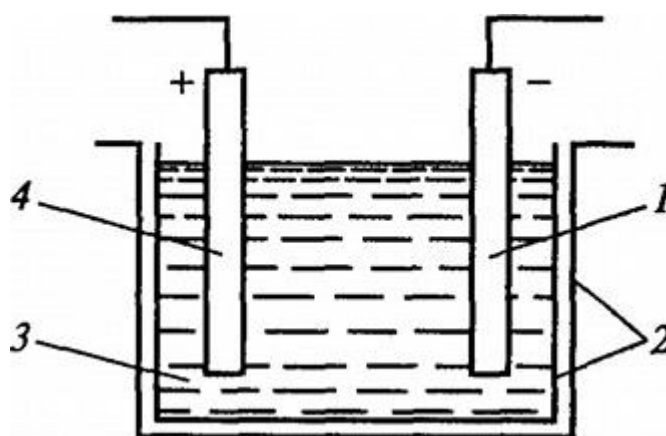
Схема электролитического восстановления детали: 1 — деталь; 2 — облицовка; 3 — электролит; 4 — анодная пластинка
